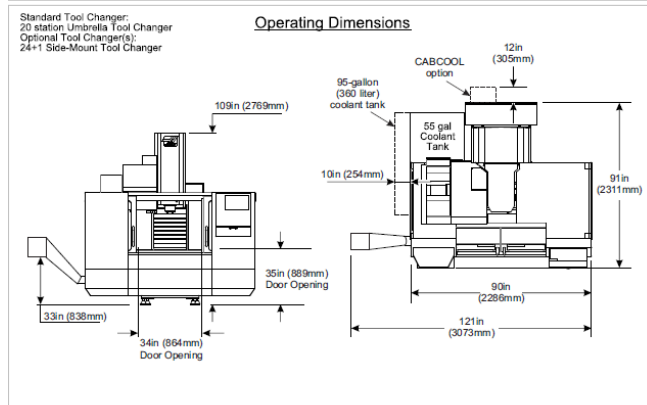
Вертикально – фрезерний верстат Haas VF-1
